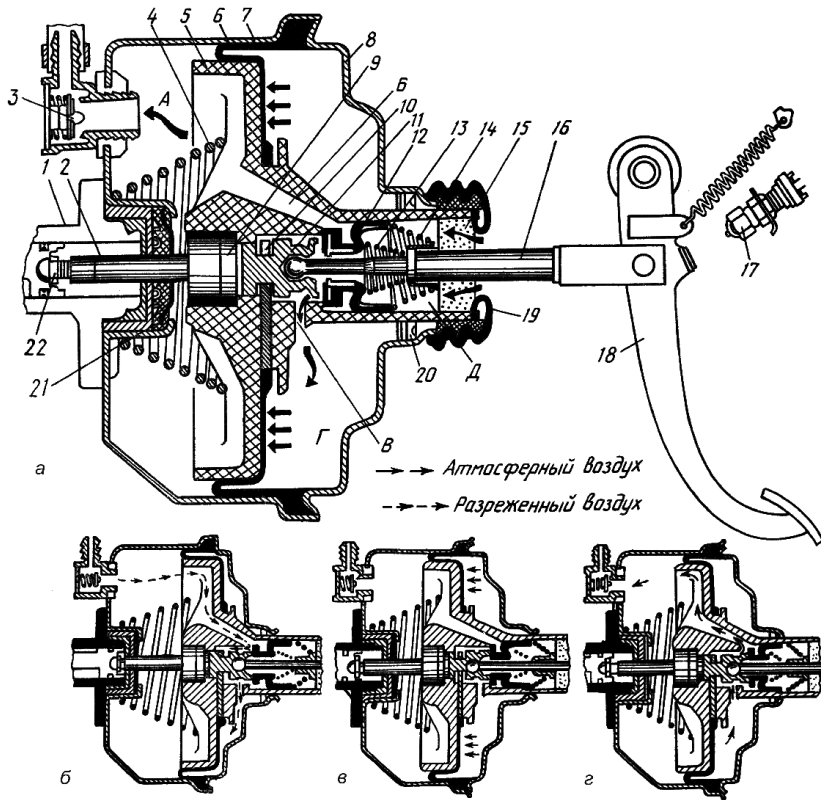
Гидروвакуумный усилитель автомобиля, конструктивно совмещенный с главным тормозным цилиндром:
